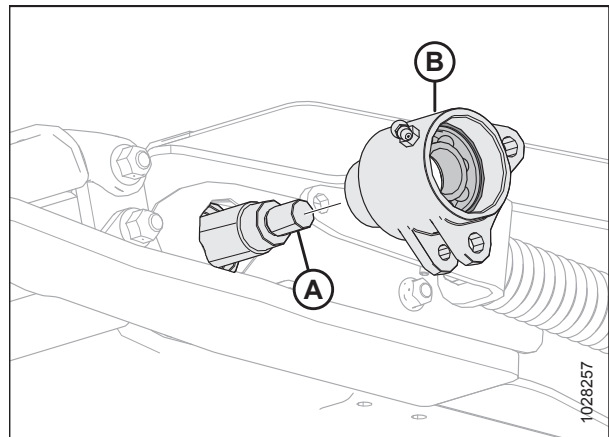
Rodamiento de rodillo tensor: lado izquierdo
